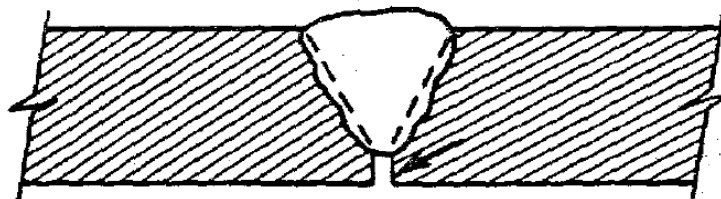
Falta de penetración en raíz de la soldadura.
